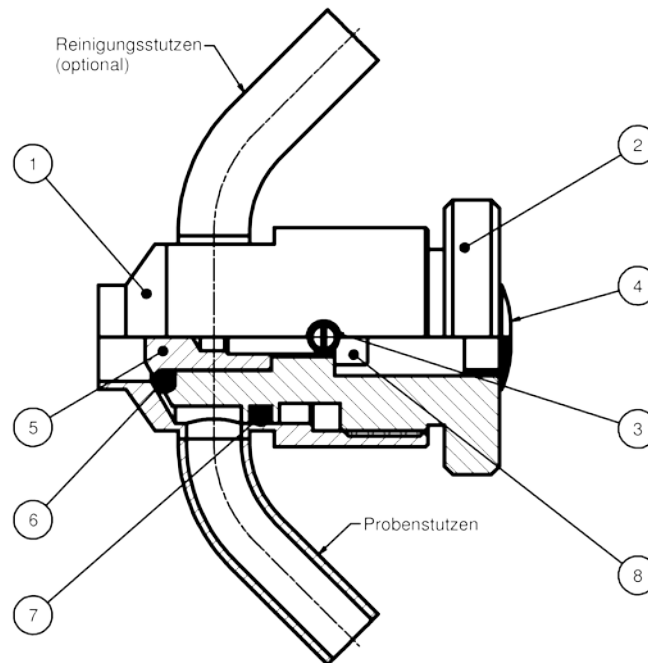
Schnitt Probenehmer mit O-Ring (Abmessungen siehe Kapitel 10.1)
